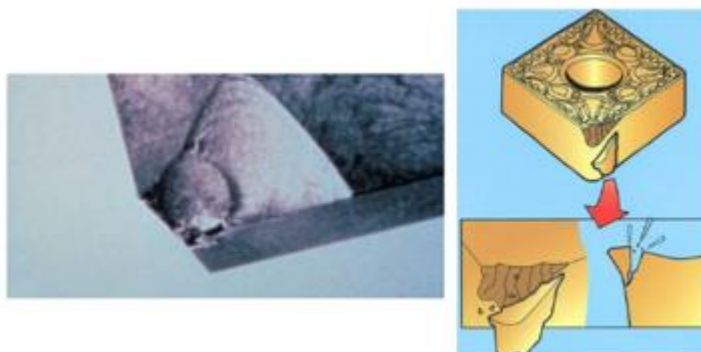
Inserto que sofreu quebra no momento da usinagem
